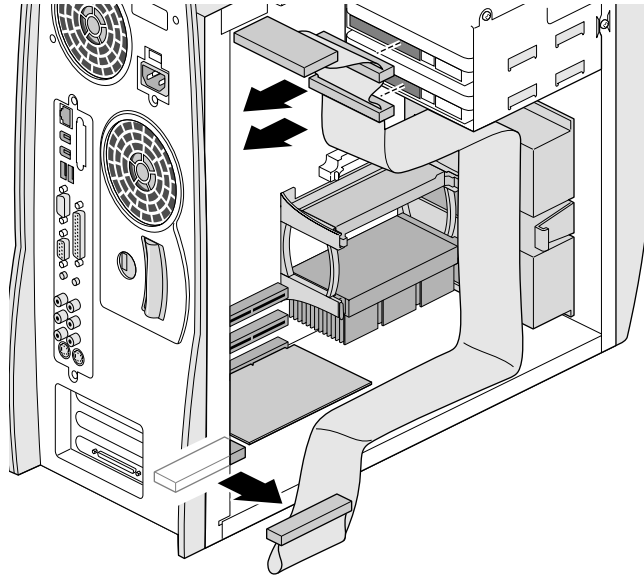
Conectando o Cabo Interno da Placa Opcional SCSI PCI
